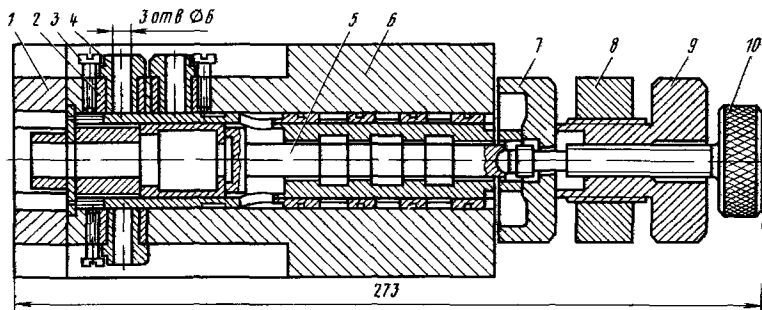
Кондуктор для сверления трех отверстий в буксе регулятора
